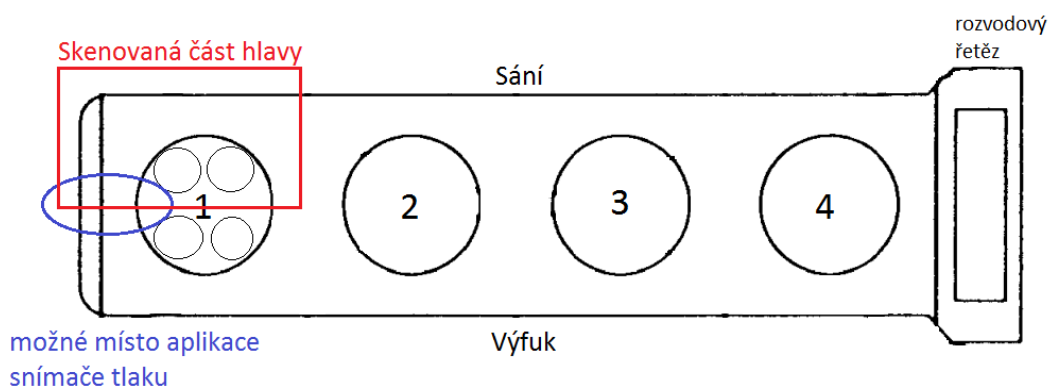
Spalovací prostor hlavy motoru Yamaha YZF-R6
